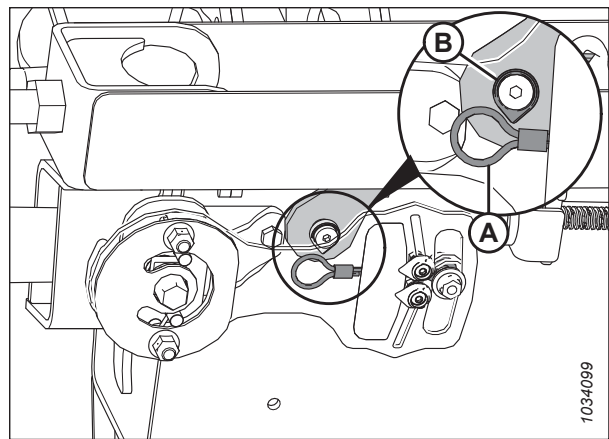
Serrure à câble FlexChecker - Côté gauche
